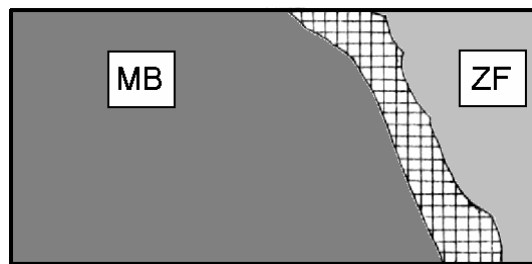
Maillage de la ZAT pour la soudure initiale (S1)
